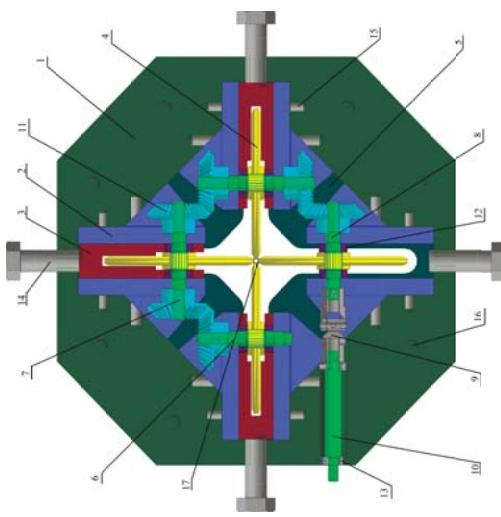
Конструкція 4-х валкової кліп для профілювання внутрішньої поверхні трубчастої заготовки:
